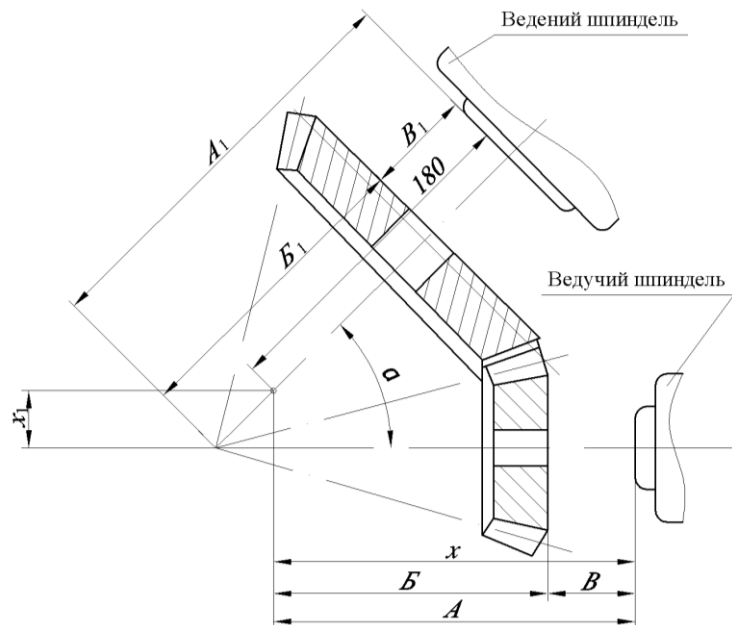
Розрахункова схема розміщення неортогональних зубчастих конічних формуючих інструментів
